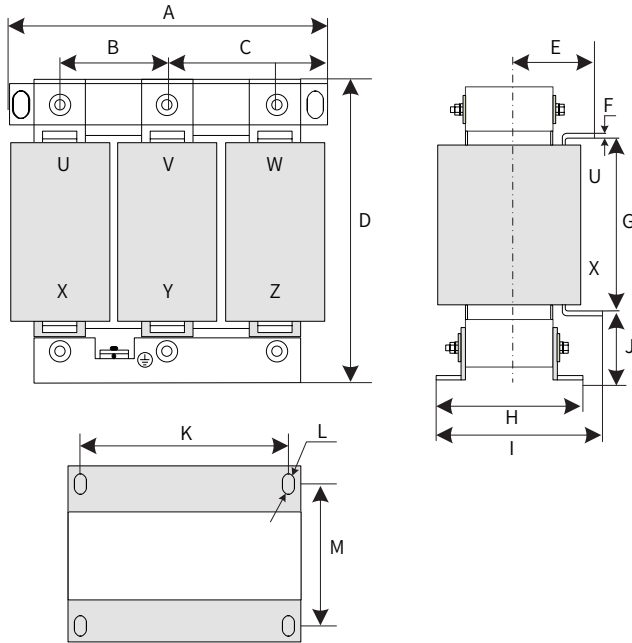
Размеры выходного реактора переменного тока 150 - 250 А
